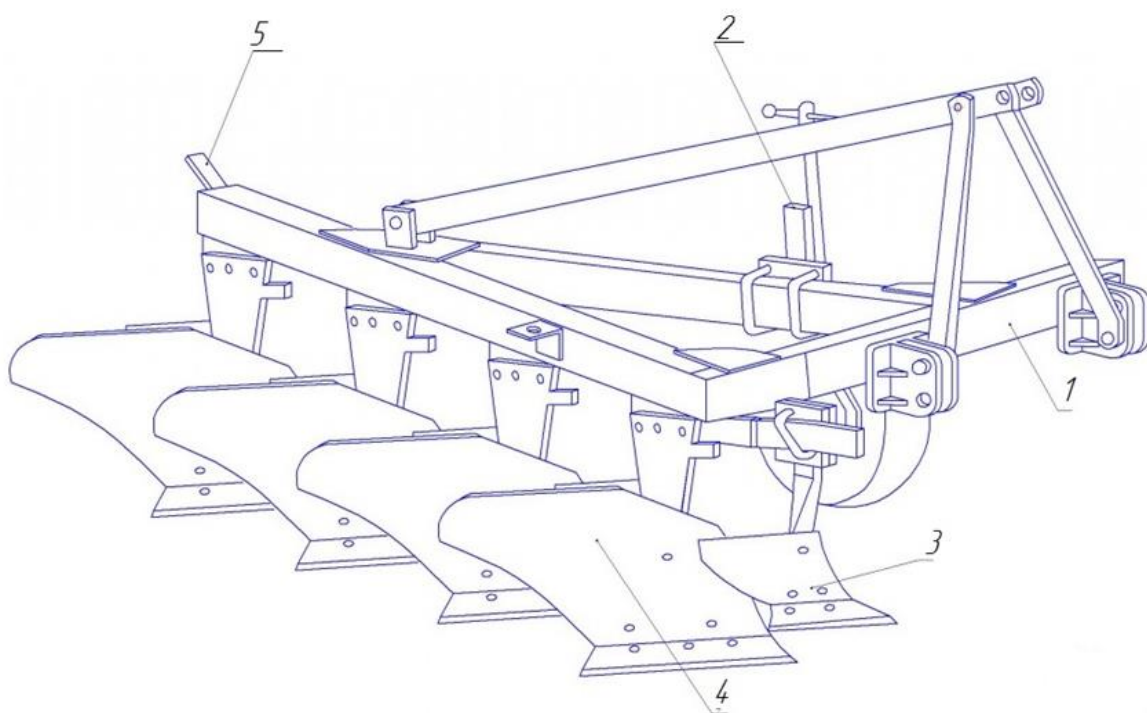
Плуг чотирьохкорпусний начіпний ПЛН-4-35: 1 – рама; 2 – корпус; 3 – світлоповертач; 4 – передплужник; 5 – колесо.
